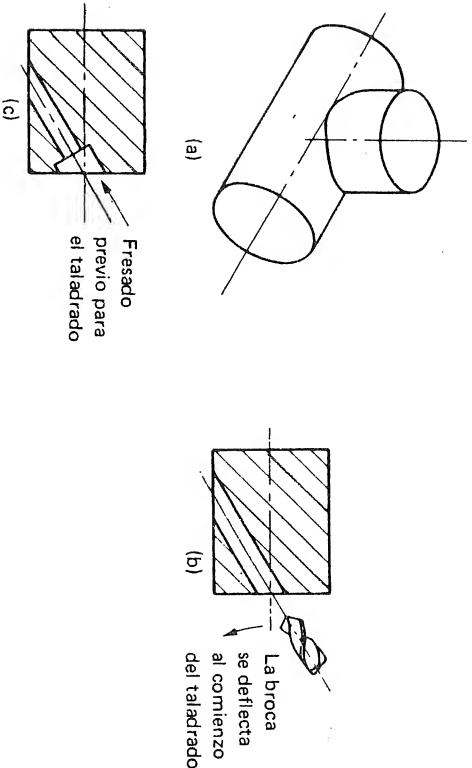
Dificultades que surgen cuando se especifican superficies cilíndricas no concéntricas. a) Imposible de mecanizar; b) difíciles de mecanizar; c) pueden mecanizarse en una taladradora.
